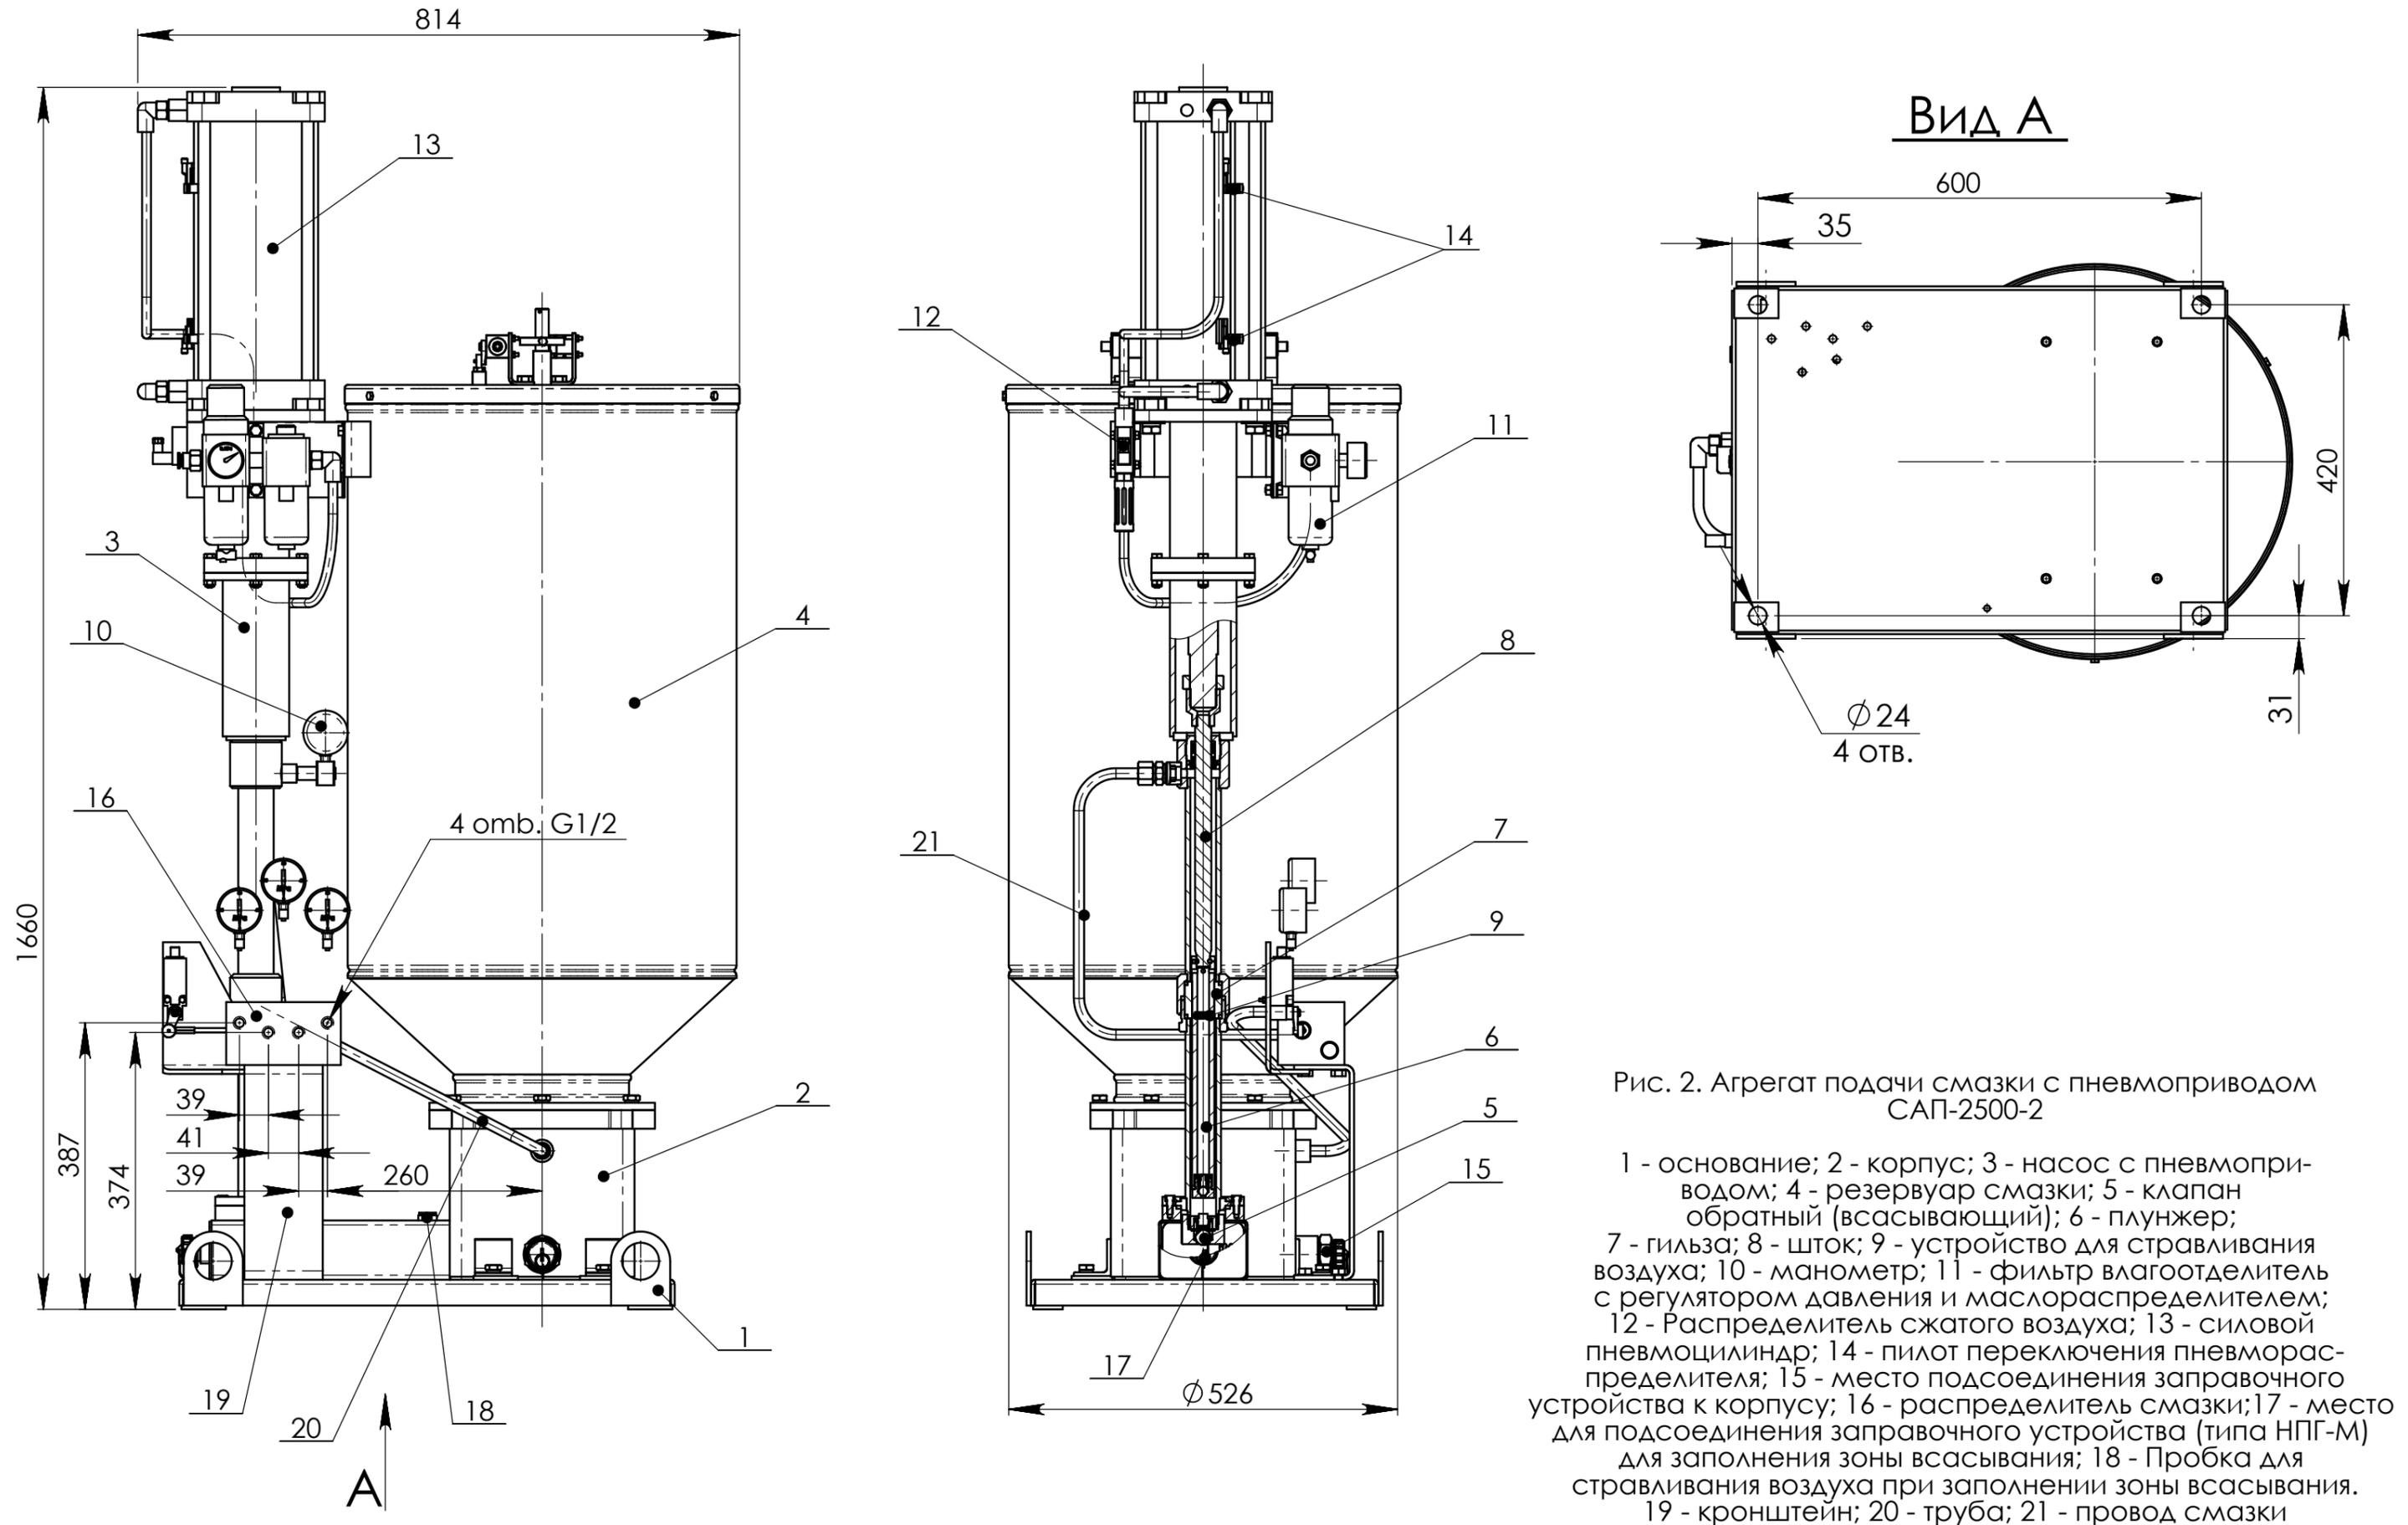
Агрегат подачи смазки с пневмоприводом САП-2500-2
